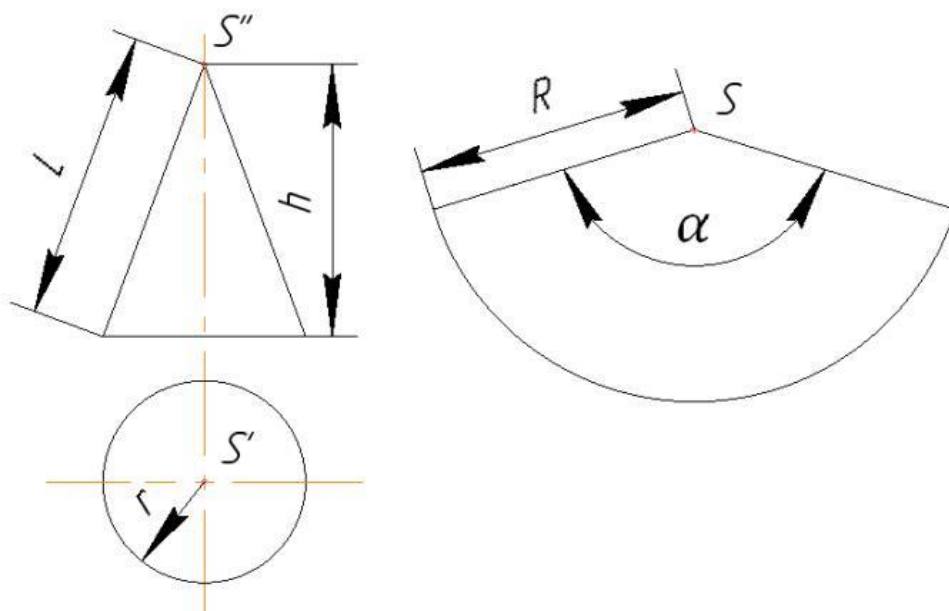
Развёртка боковой поверхности конуса вращения
